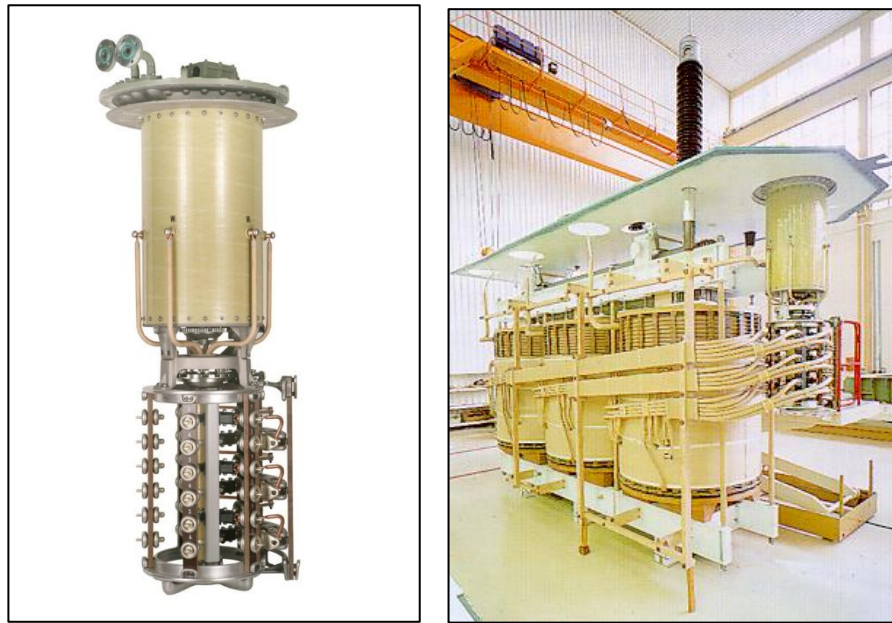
Regulador em carga Maschinenfabrik Reinhausen Tipo Oiltap M e seu exemplo de instalação num transformador EFACEC.
